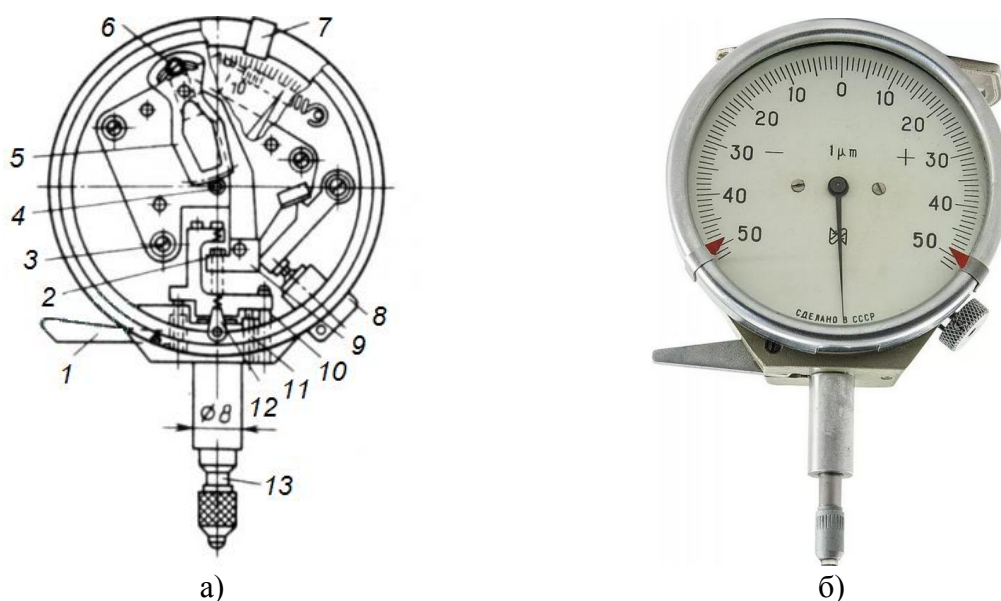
Кинематическая схема и внешний вид рычажно-зубчатой головки 1ИГ
